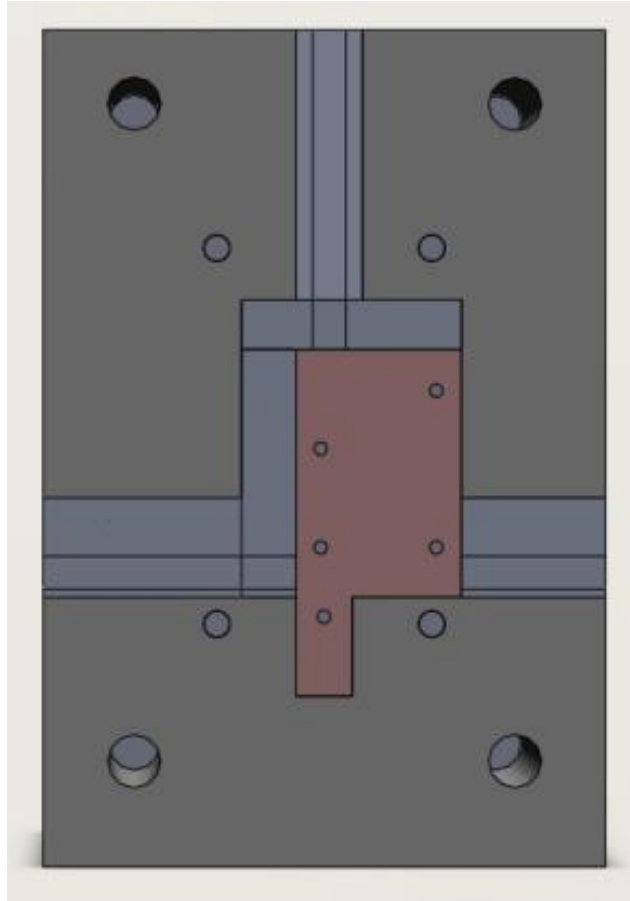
Vista en planta de la configuración de llenado por pared corto.
